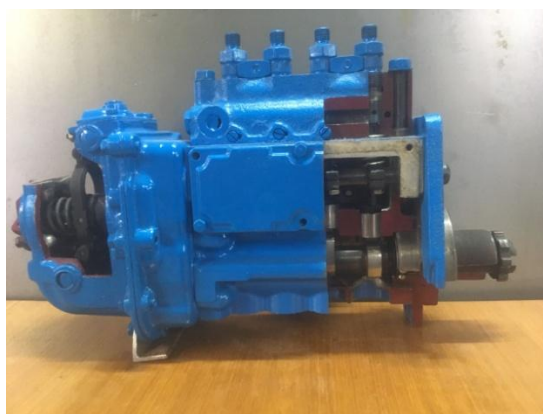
Стенд с разрезом, демонстрирующим кулачковый вал, рейку и ось рычага рейки
